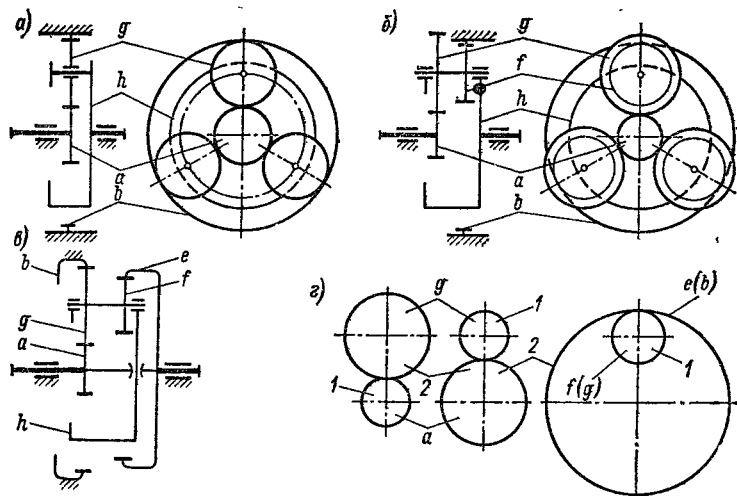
Схемы планетарных передач: *a* — тип 2К-*h*, схема А; *б* — тип 2К-*h*, схема В; *в* — тип 3К; *г* — примеры условного обозначения зубчатых колес *a* — центральные зубчатые колеса с внешними зубьями; *b, e* — то же с внутренними зубьями; *g, f* — сателлиты; *h* — водило; 1 — шестерня; 2 — колесо
